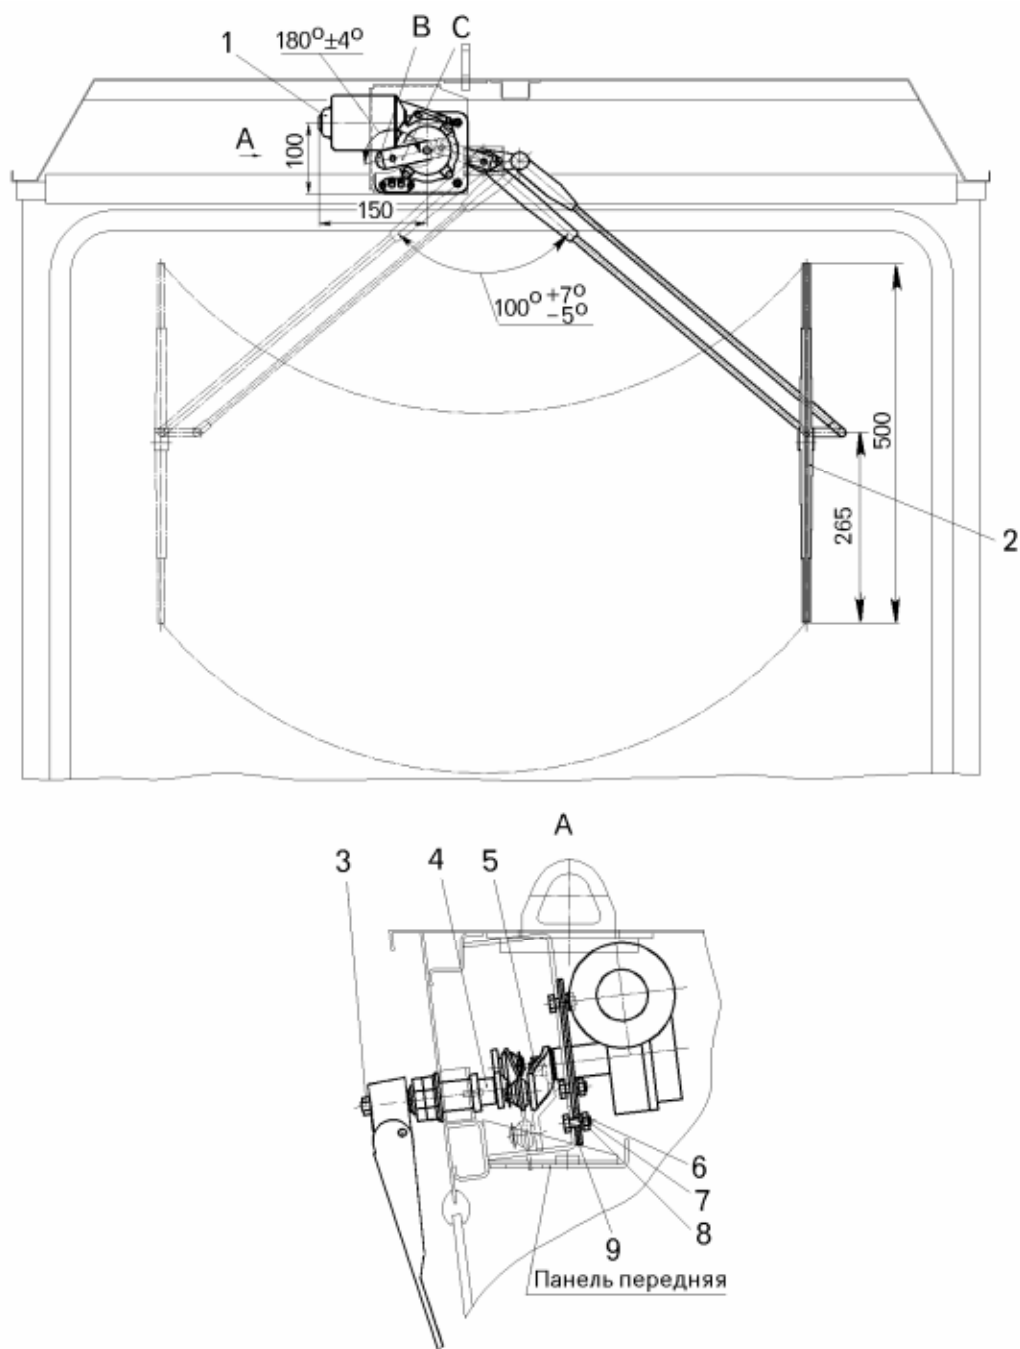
Установка стеклоочистителя, рычага и щетки (вид из кабины):
